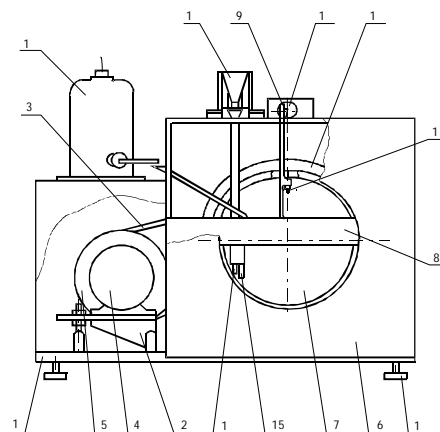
Схема прибора РСЗ-2, где 1 – сварное основание, 2 – натяжное устройство, 3 – приводной ремень, 4 – электродвигатель, 5 – трехручьевые шкивы, 6 – крышка защитного кожуха, 7 – окно, 8 – поперечная планка, 9 – упругая балка, 10 – образец, 11 – ножка механотрона, 12 – питатель, 13 – колба Вульфа, 14, 15 – направляющие
